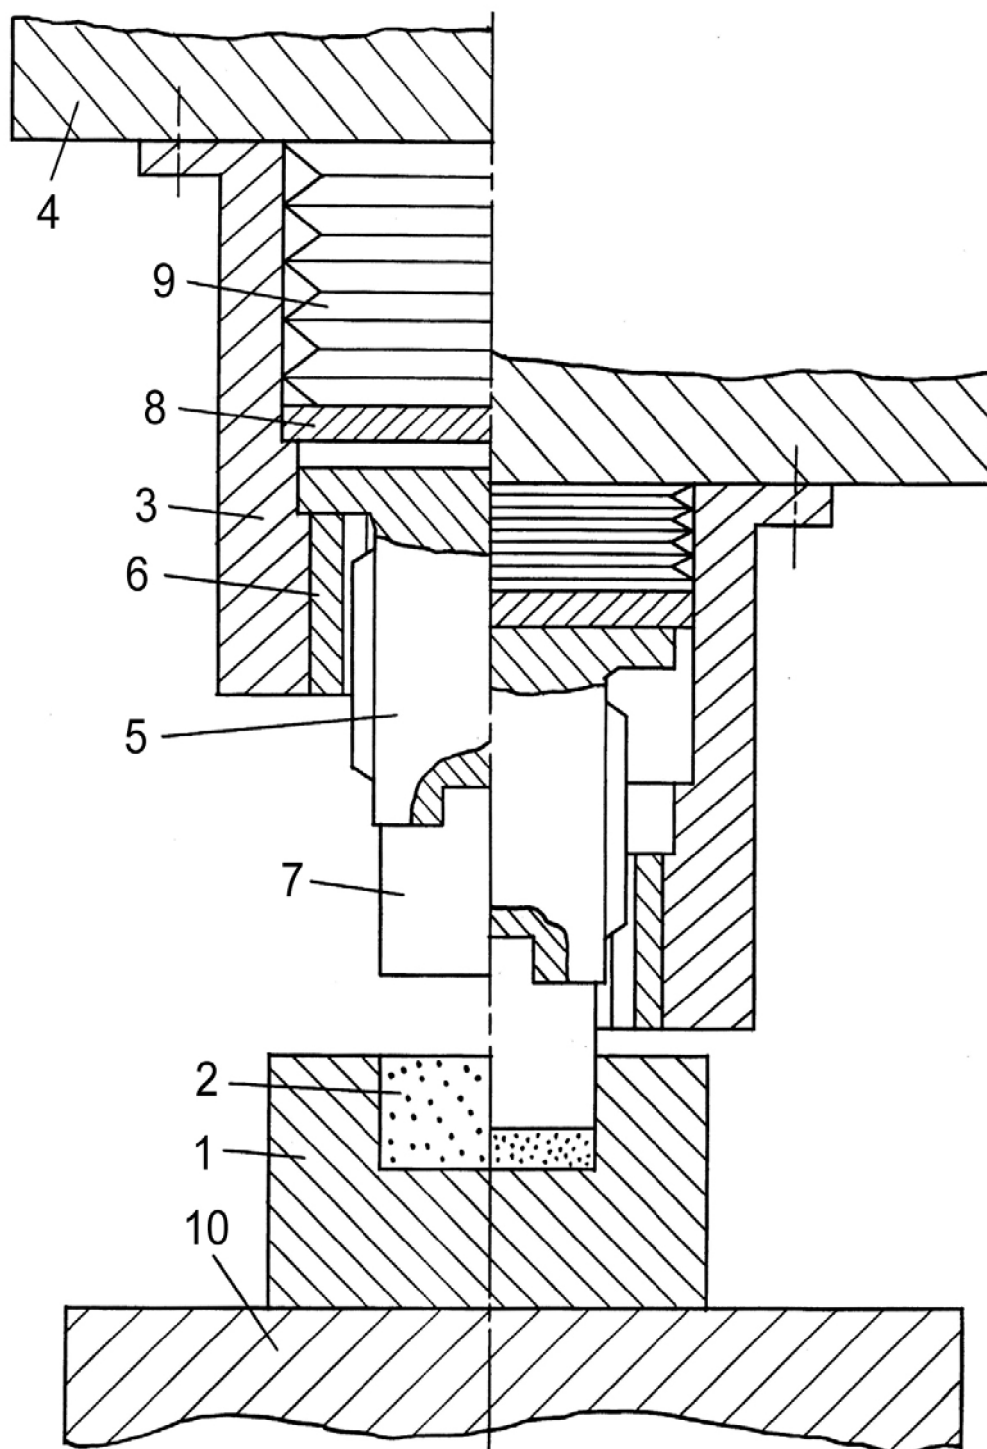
Конструкция штампа для уплотнения заготовки поворачивающимся пуансоном
